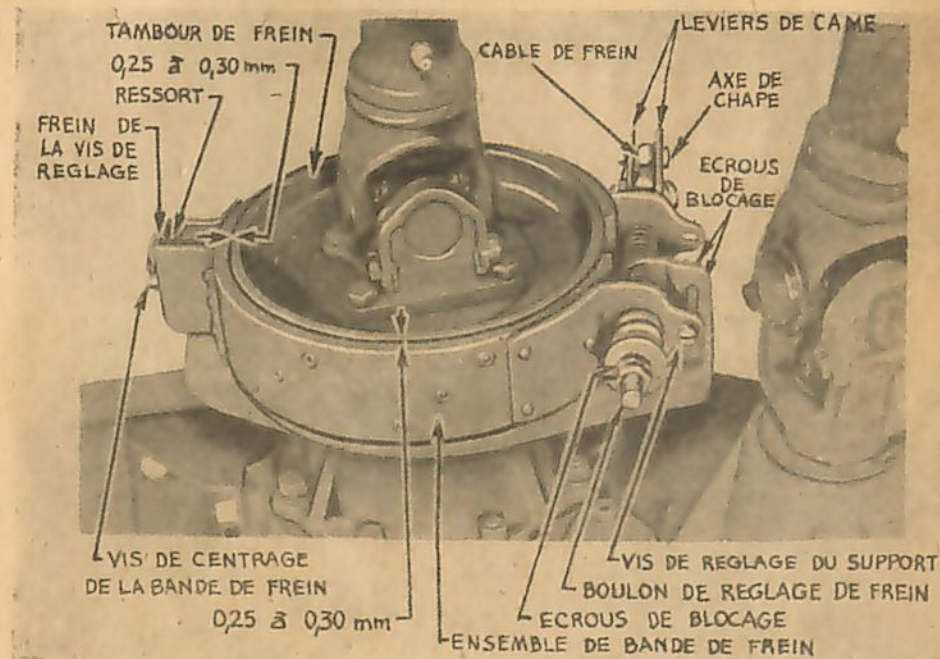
Vue du frein à main sur châssis 1 1/2 T. 6 x 6.
